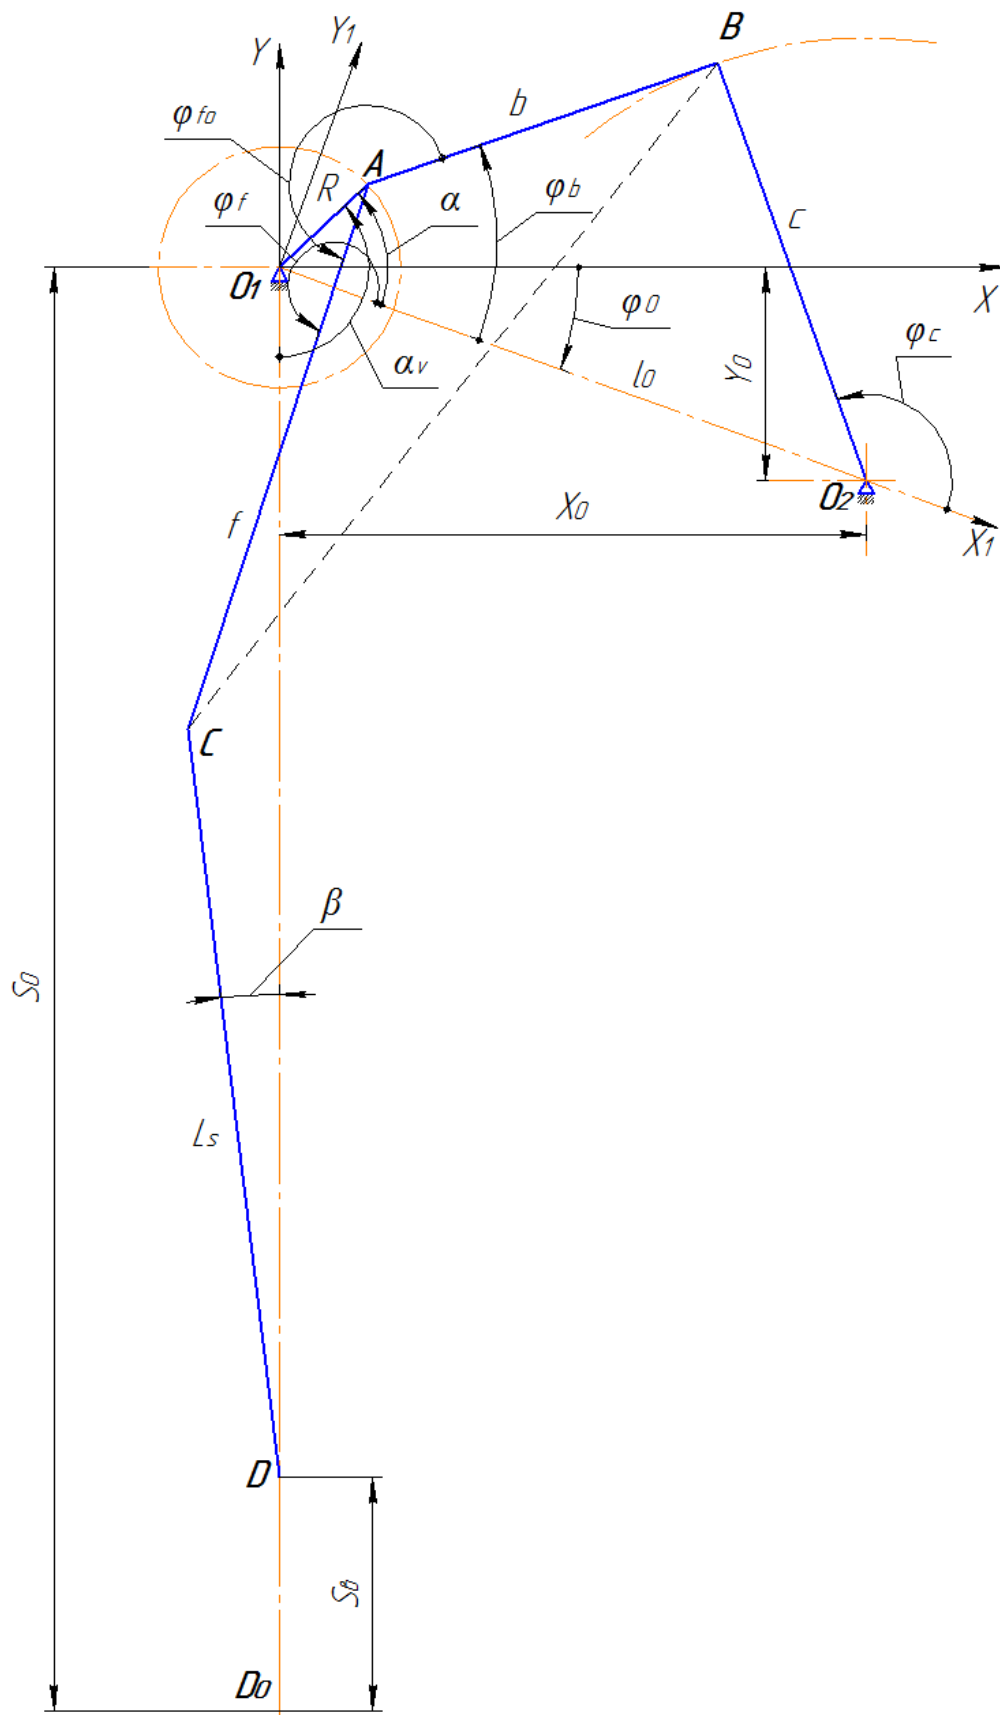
Розрахункова схема шестиланкового механізму внутрішнього повзуна витяжних пресів
